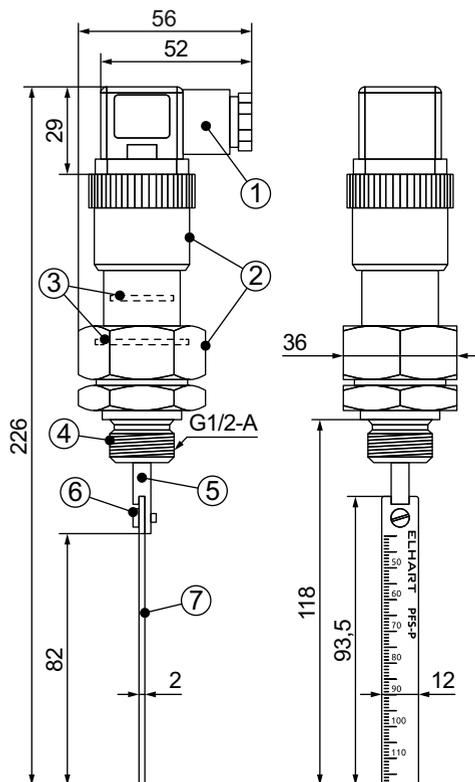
Габаритные размеры реле и сменного лепестка,
